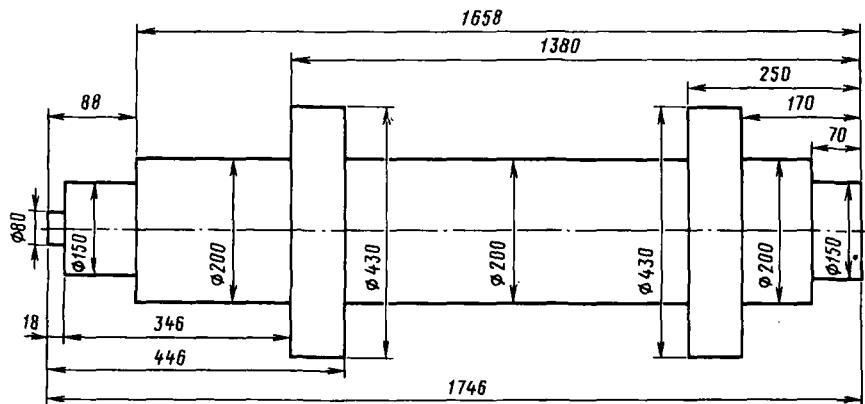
Упрощенный чертёж главного приводного вала эскалатора ЛТ-5
